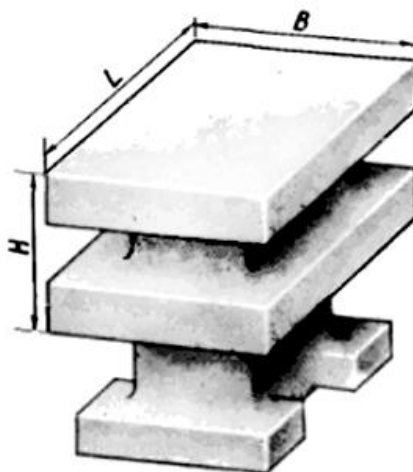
Форма образца для проверки точности вертикально-фрезерного станка
